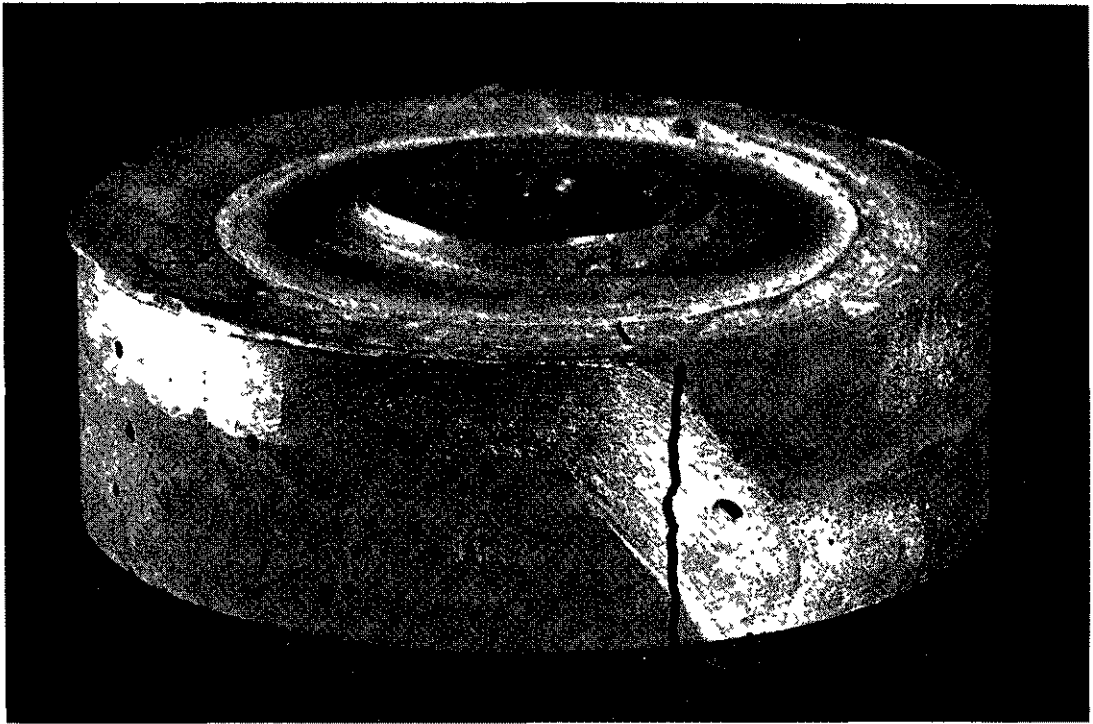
Anneau de fissurabilité montrant l'ouverture de la fissure
